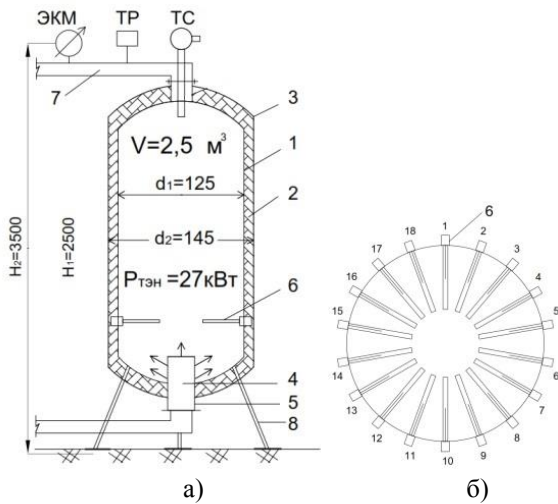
а) устройство напорного бойлера; б) схема расположения ТЭНов
